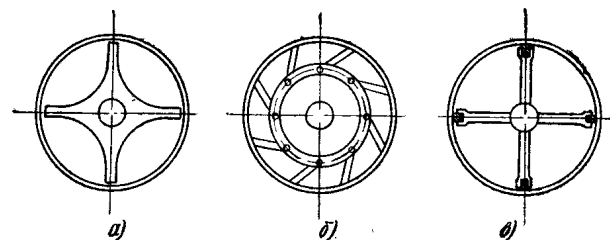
Типы роторных мешалок: а — жесткие; б — с шарнирно закрепленными лопастями; в — с подвижными скребками
